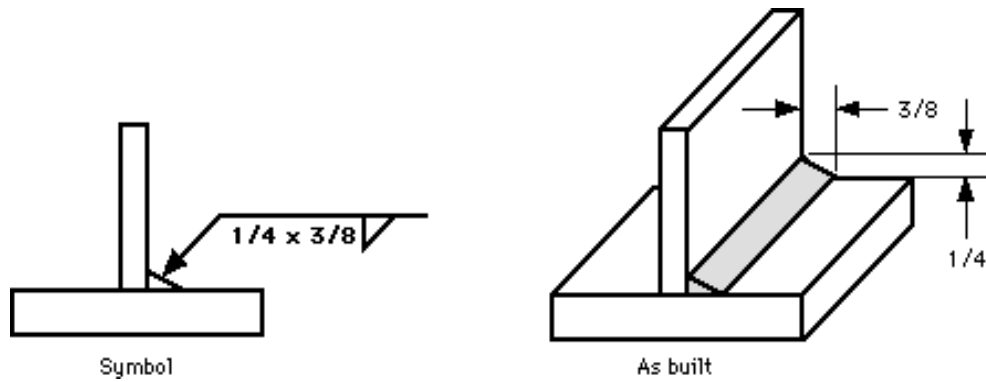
Soldadura de Filete (Caras Desiguales).<sup>17</sup>
